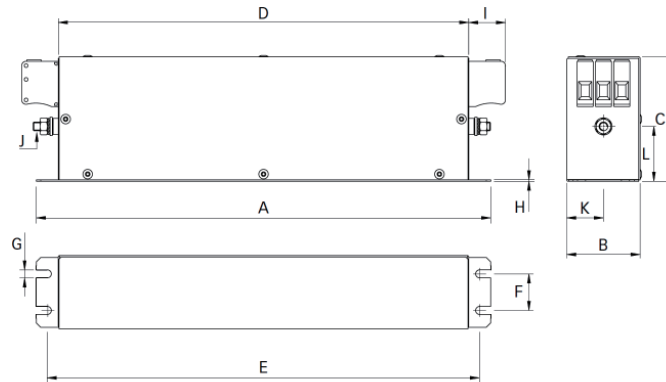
Габаритный чертеж фильтров серии FN 3258 (ед. изм.: мм)
